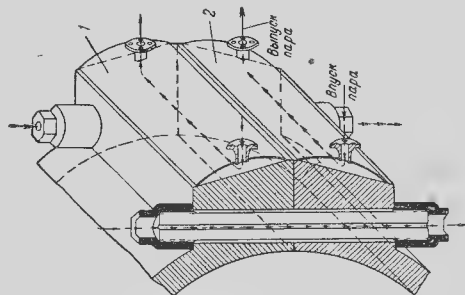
Устройство для обогрева паром фланцев и шпильки корпуса турбины в. д.
